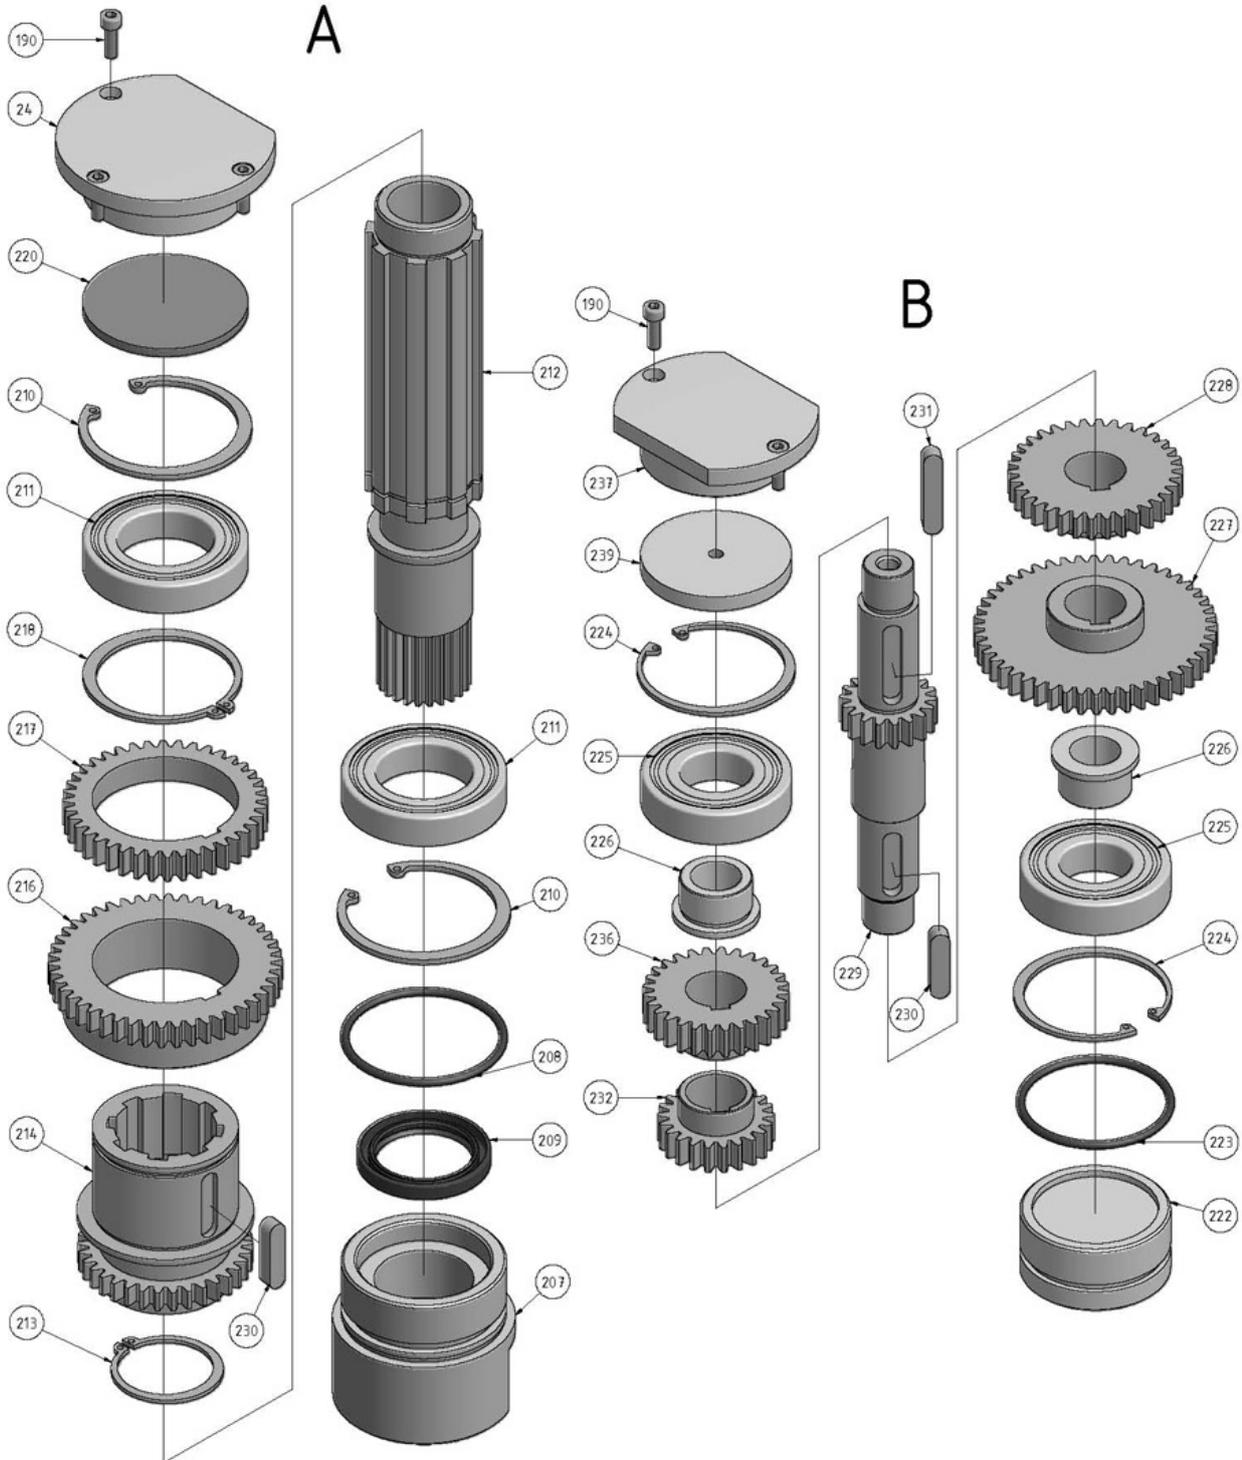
Getriebe Bohrspindel 1 von 4 - Gear box main spindle 1 von 4
